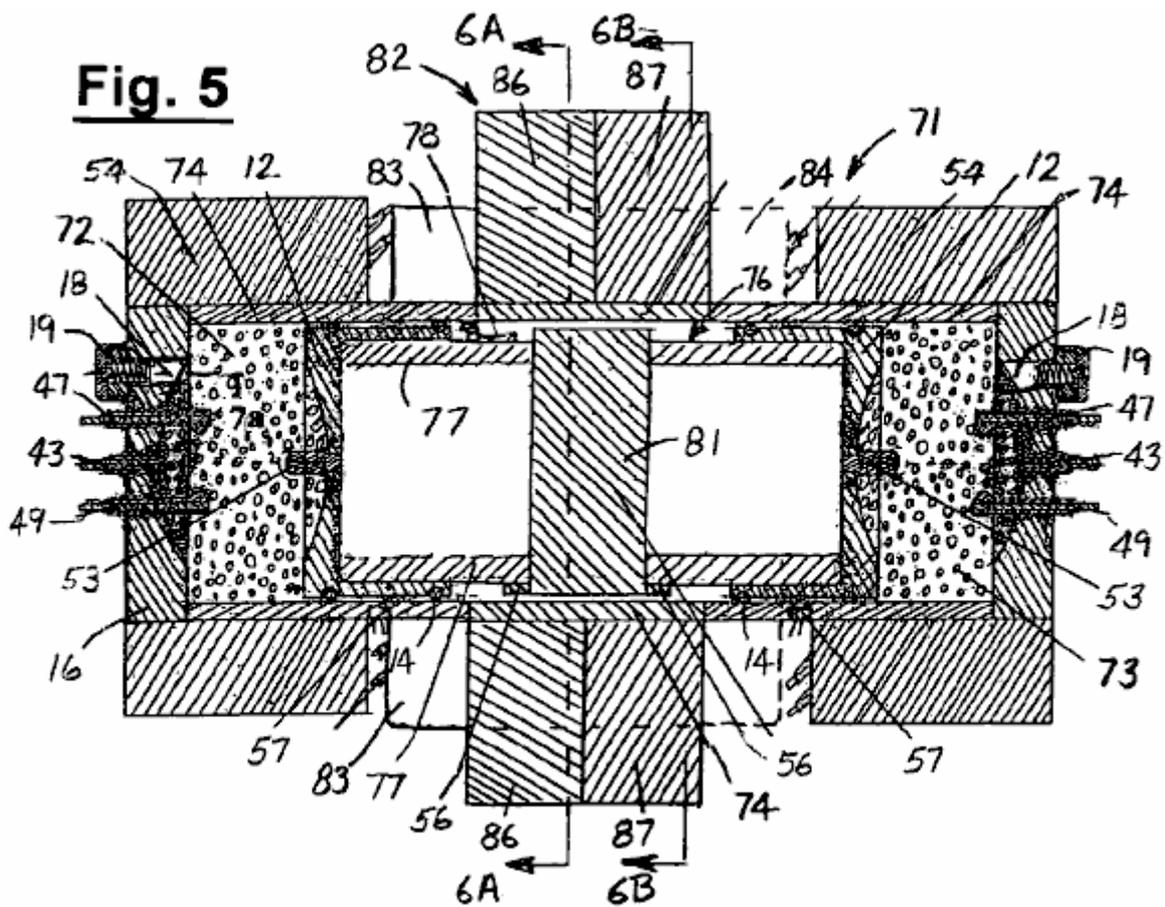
ist eine Mittellinienschnittansicht einer weiteren Ausführungsform eines internen Explosionsmotors und Generators, der die Erfindung beinhaltet.
